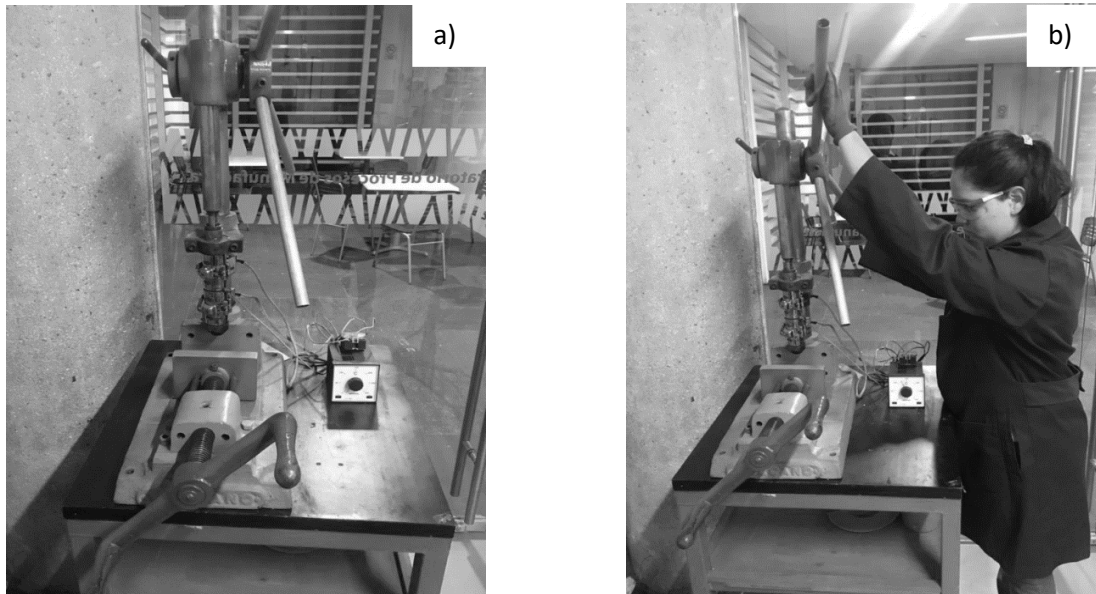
a) Máquina de inyección de la Universidad Panamericana y b) máquina de inyección en uso para fabricación de filamentos
